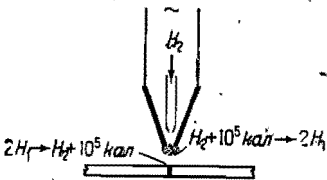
Принципиальная схема сварки помощью атомарного водорода.
